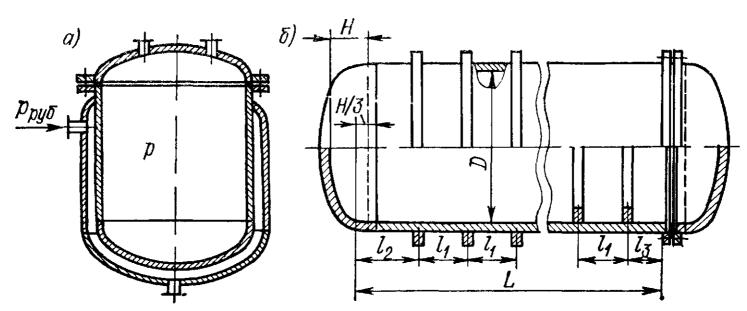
Корпус аппарата: а — с «рубашкой»; б — с кольцами жест-
